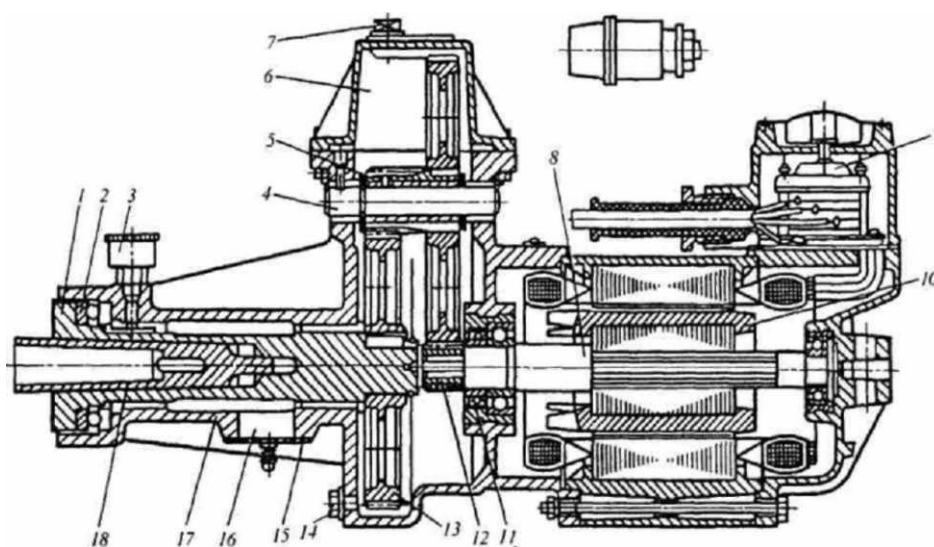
Мотор-редуктор рельсосверлильного станка 1024 В
